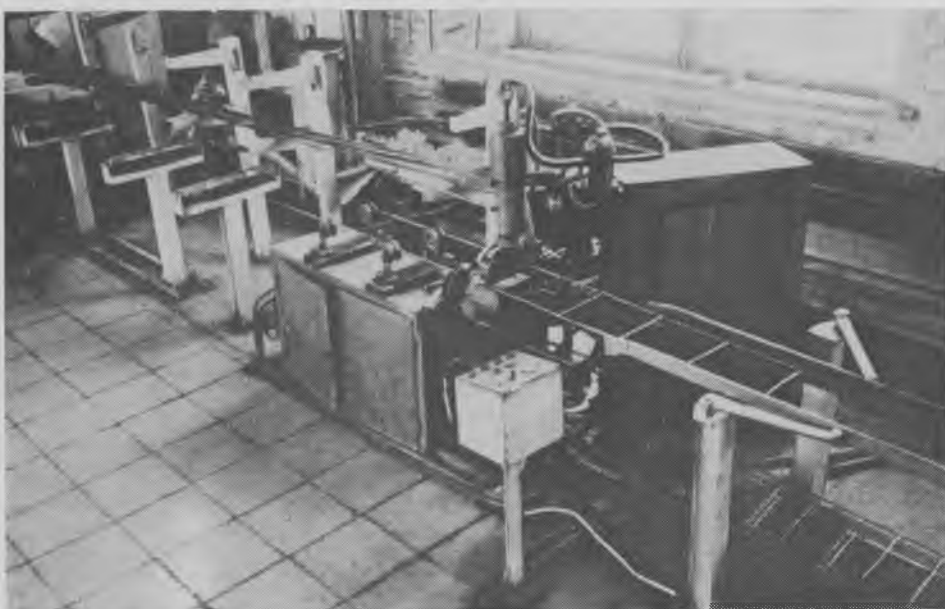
Полуавтоматическая линия для сварки средних двухветвевых каркасов (ПДС-6)
